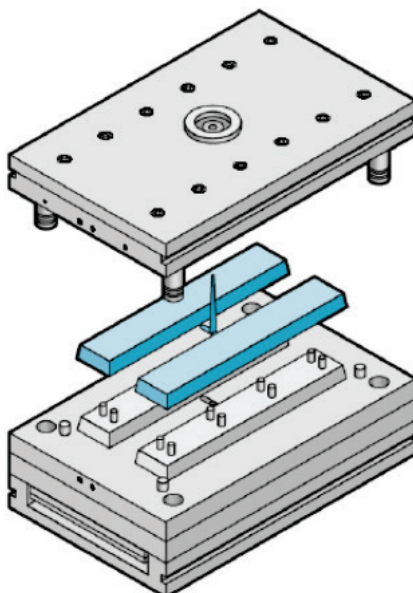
Exemplo de molde de duas placas (Part and Mold Design - A Design Guide, 2000).
